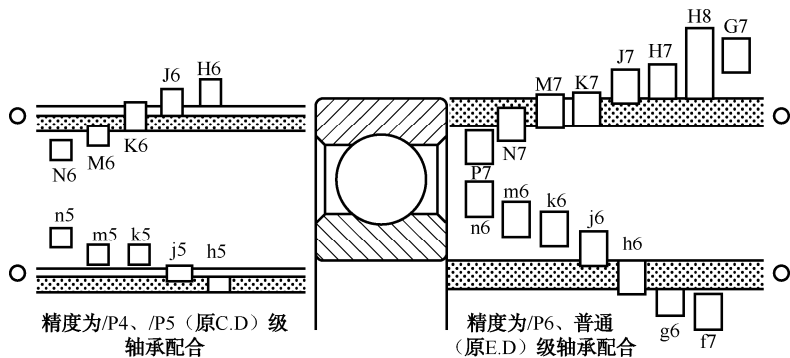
滚动轴承外圈与轴承座、滚动轴承内圈与轴的配合
